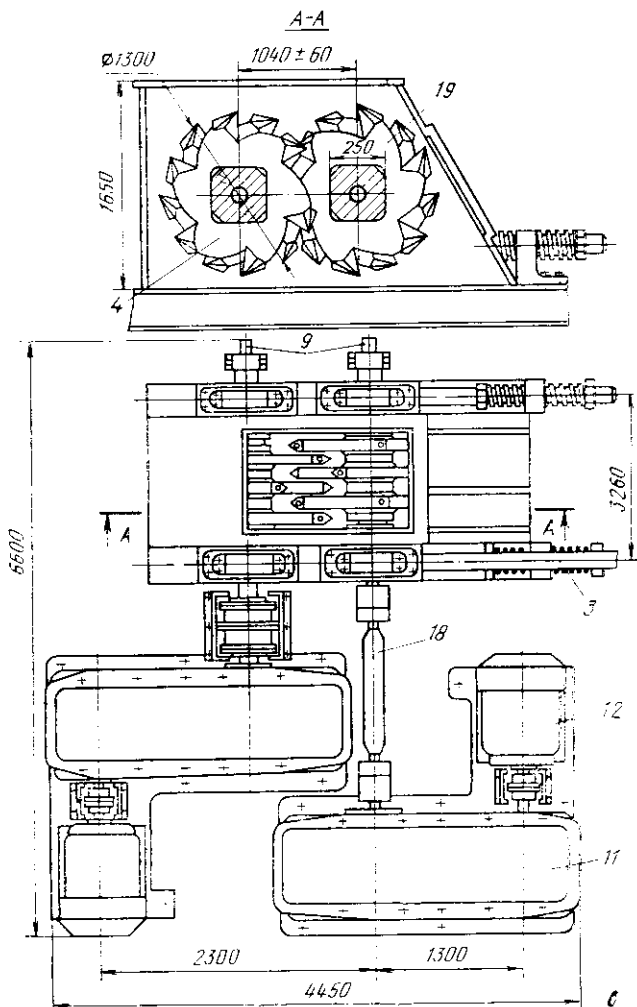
Конструкции валковых зубчатых дробилок горячего агломерата:
